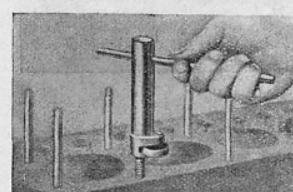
Процесс вывертывания шпильки головки блока цилиндров при помощи роликового экстрактора
